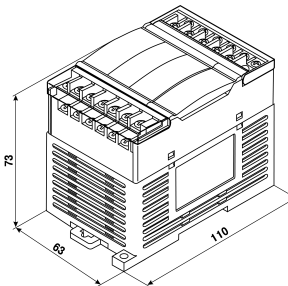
Габаритный чертеж ПР110-х.8х.4х
